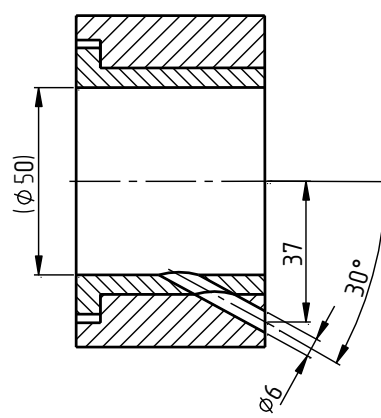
Размеры, указываемые на рабочем чертеже детали с отверстием под запрессовку втулки, приведенной на рис. 3.183 (охватываемая деталь)
